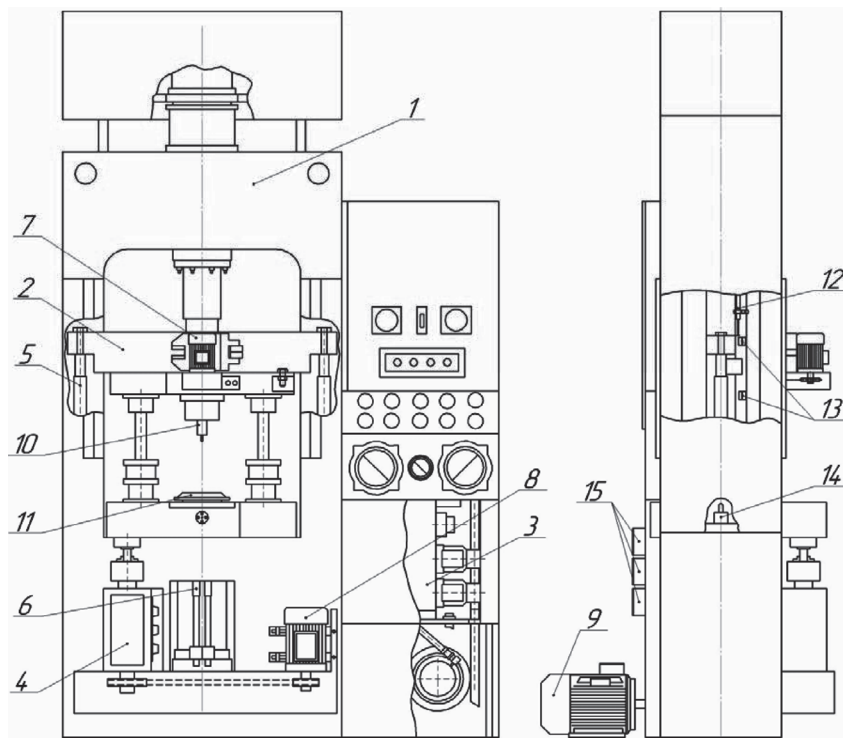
Установка валковой штамповки: 1 – гидравлический пресс; 2 – ползун; 3 – гидроагрегат; 4 – коробка передач; 5 – цилиндры возврата; 6 – выталкиватели; 7–9 – асинхронные двигатели; 10 – пуансон; 11 – приводные валки; 12 – датчик перемещения; 13 – концевые выключатели; 14 – датчик усилия; 15 – частотные преобразователи
